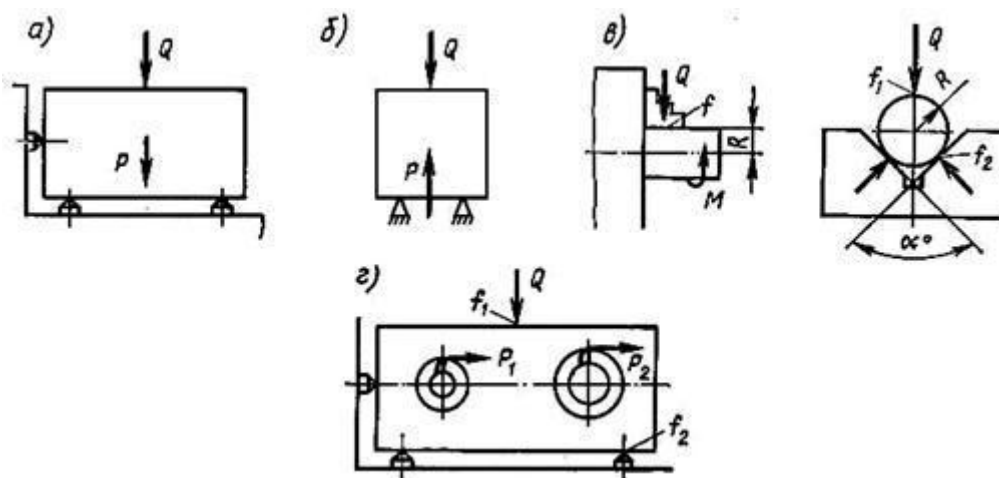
Схемы установки заготовок и определения сил зажима
